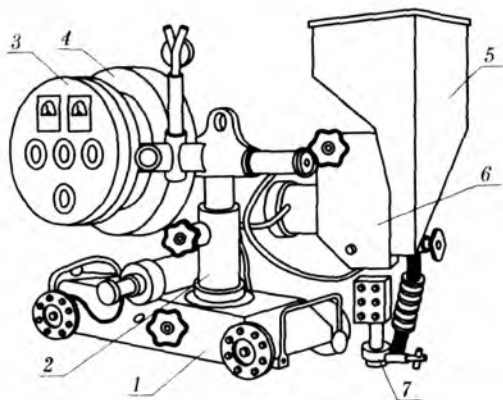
Схема сварочного трактора для автоматической сварки:
